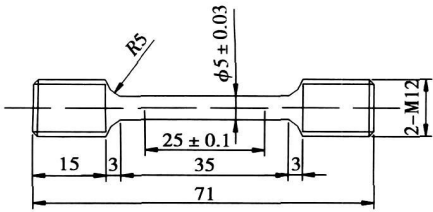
圆形带螺纹拉伸试样尺寸 (mm)
